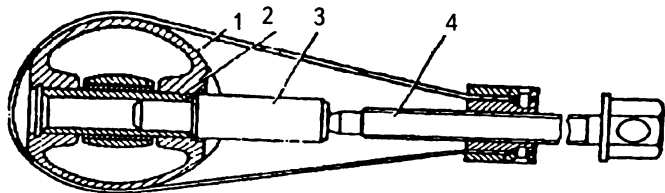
Выпрессовка поршневого пальца из поршня съемником:
